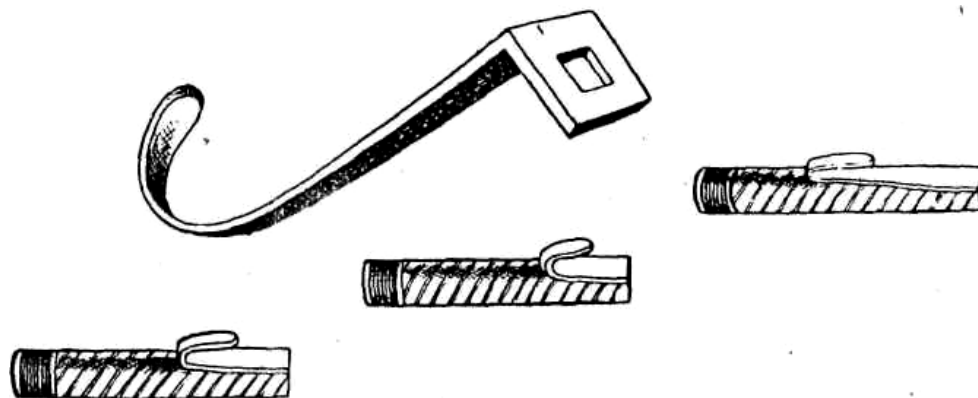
Скобы различной длины и их крепление к рукояткам.
